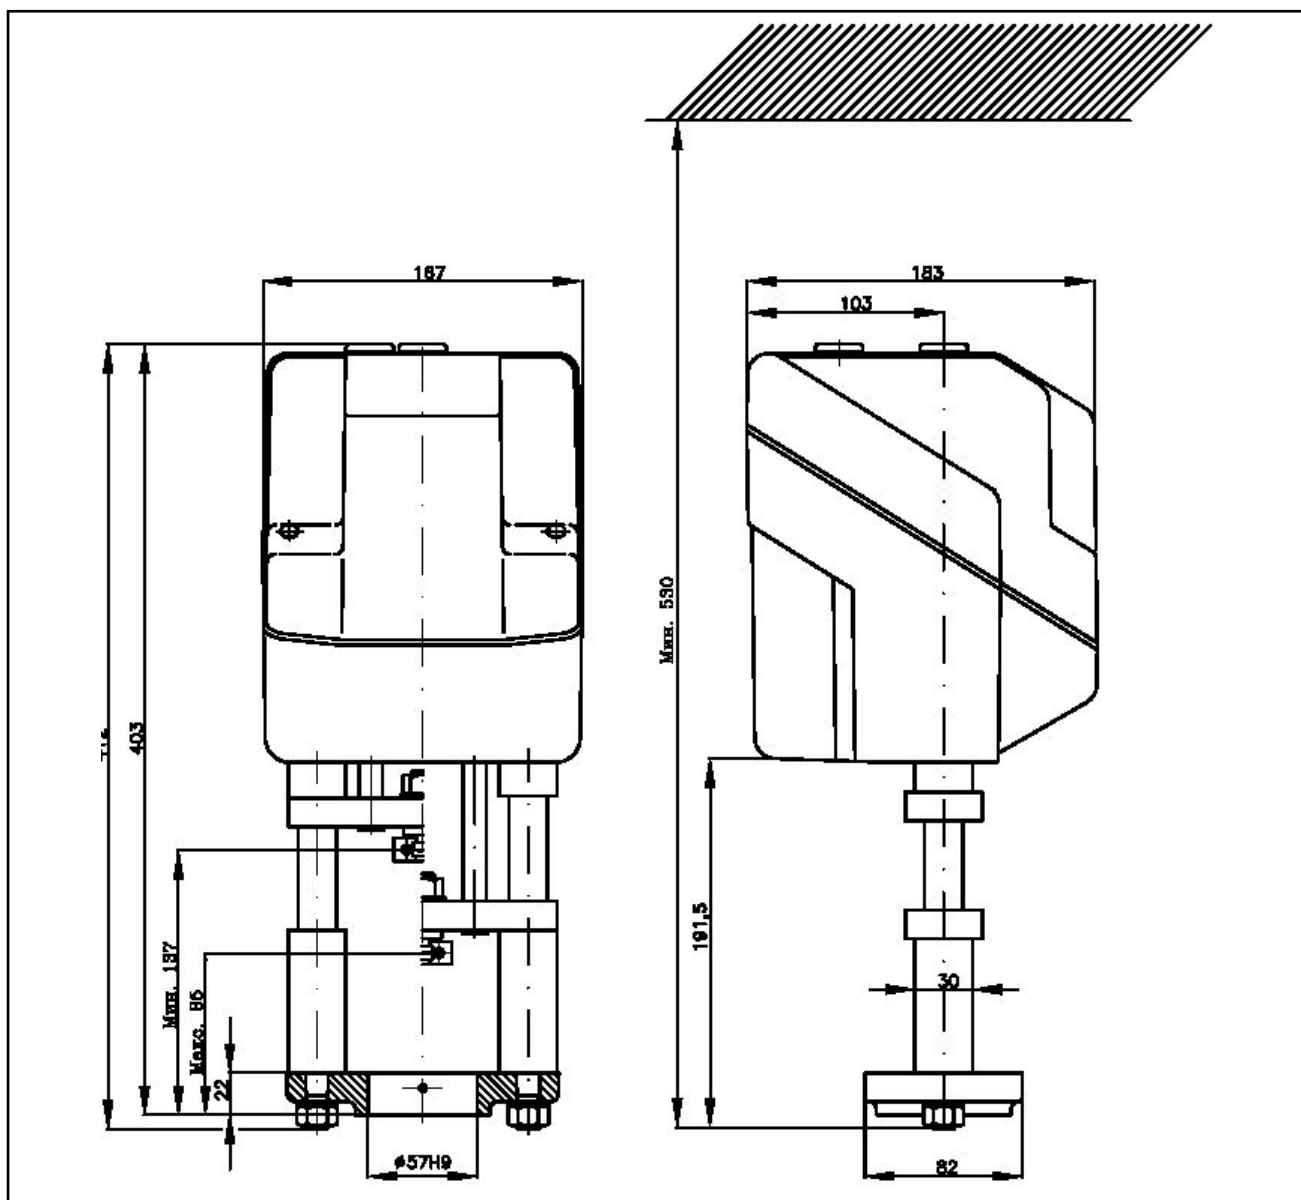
Габаритные и присоединительные размеры AMV 85, 86.
